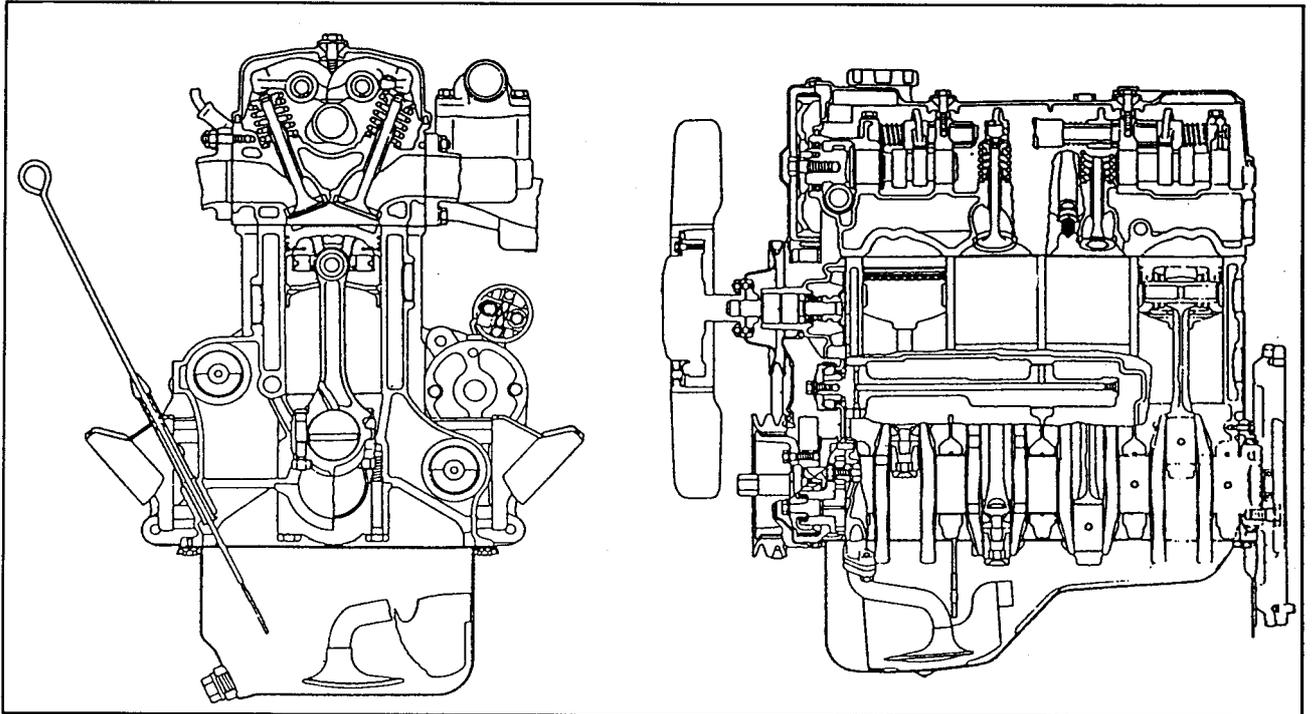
Поперечный и продольный разрезы двигателя 4G6
